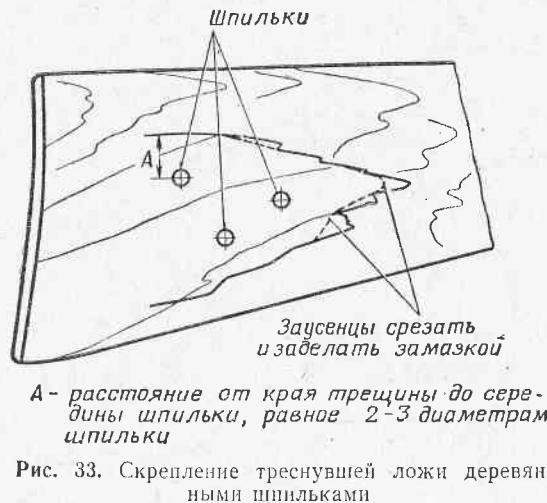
Скрепление треснувшей ложи деревянными шпилками
